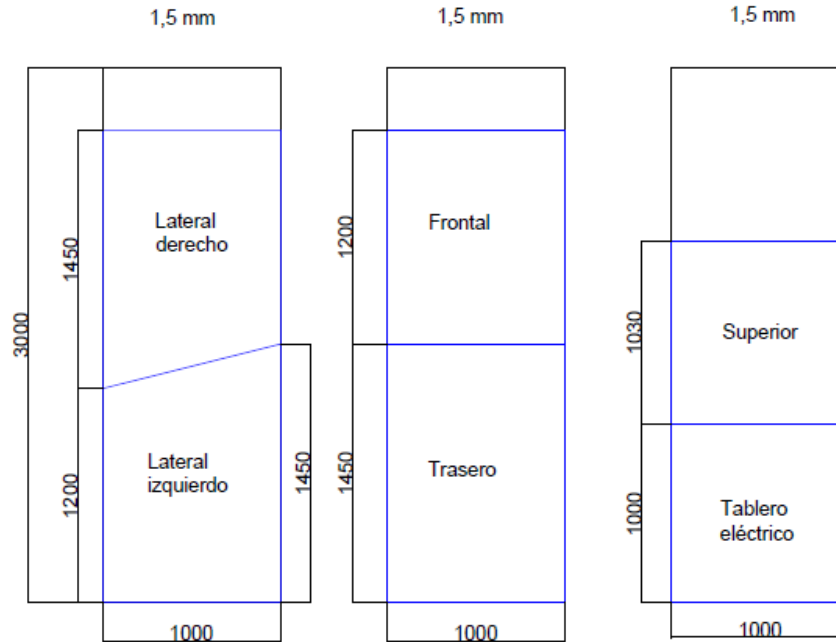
Dimensiones de tapas metálicas fabricadas con planchas de acero galvanizado de 1,5 mm.
